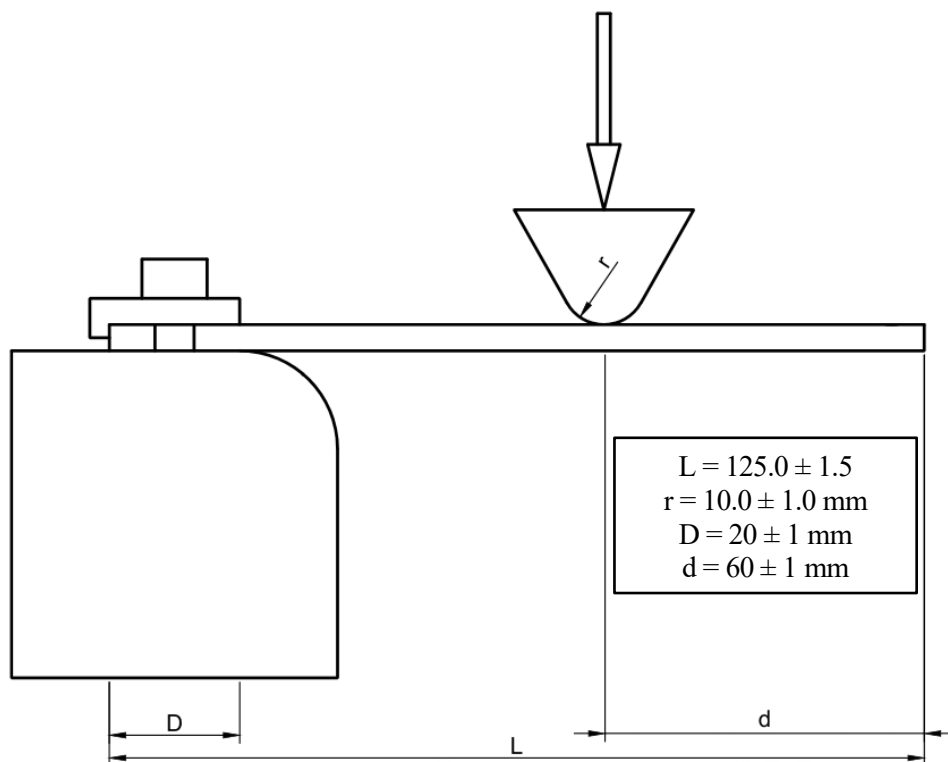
Dimensiones principales del montante de la probeta de ensayos
